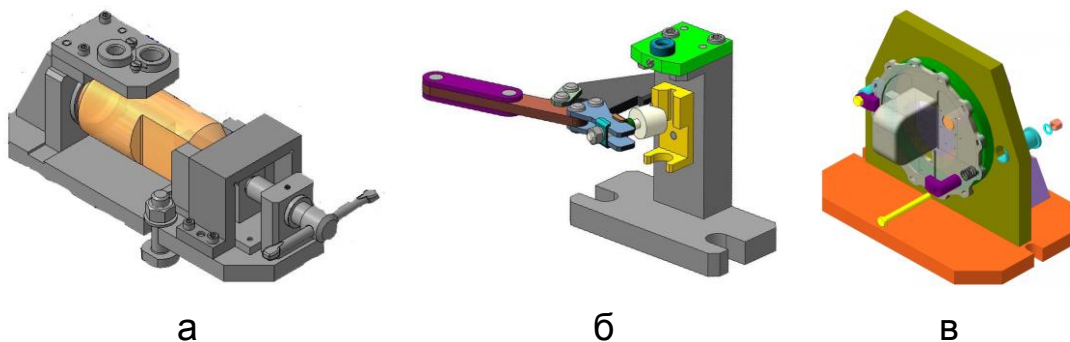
Приклади компонування корпусів спеціальних верстатних пристроїв: а, б – кондуктора; в – пристрою для фрезерування
